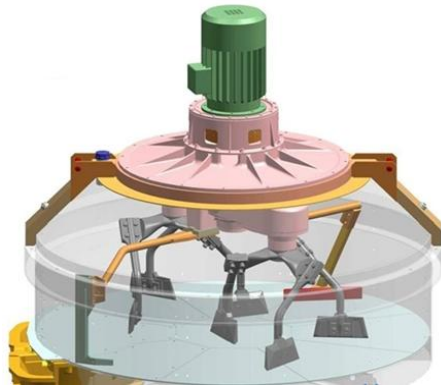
Конструкція серійного роторно-планетарного змішувача
